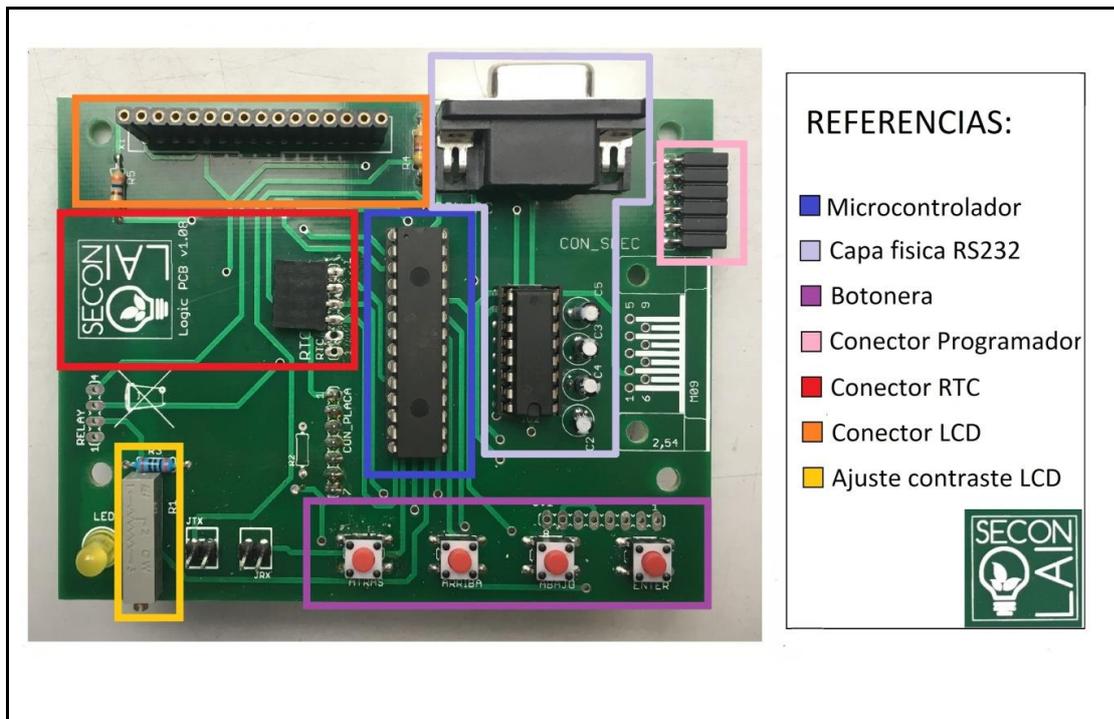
MÓDULOS EN PCB DE LÓGICA
